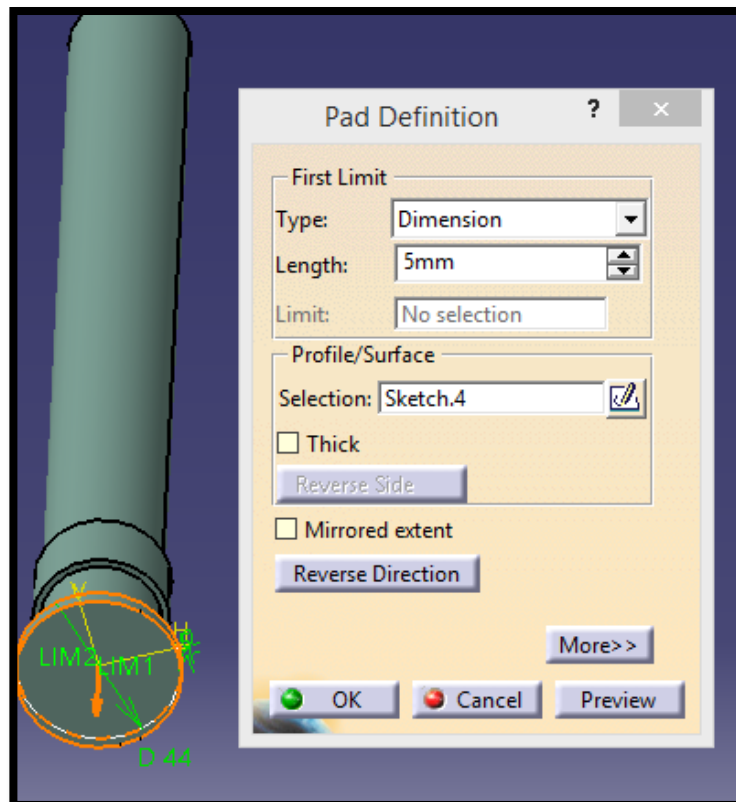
Seat mounting frame 11: Pad.4 barra inferior 2
